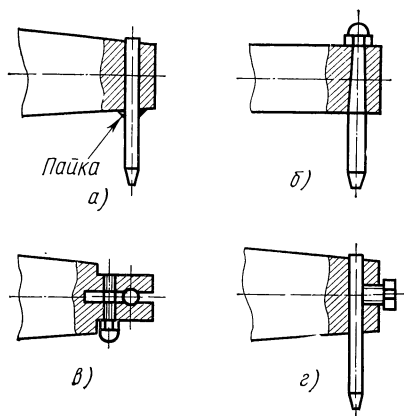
Варианты крепления ультразвуковых сварочных инструментов:
